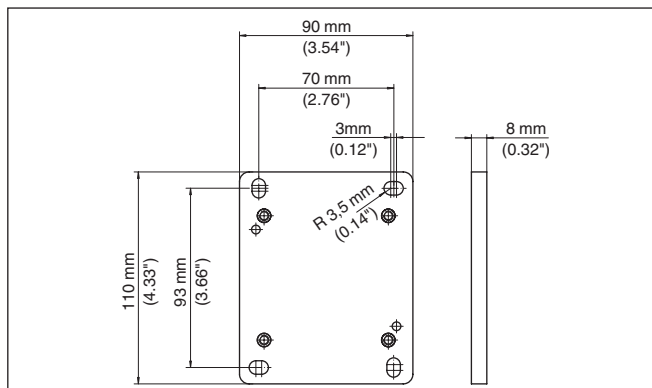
Схема отверстий - планка для настенного монтажа (выносной корпус)
